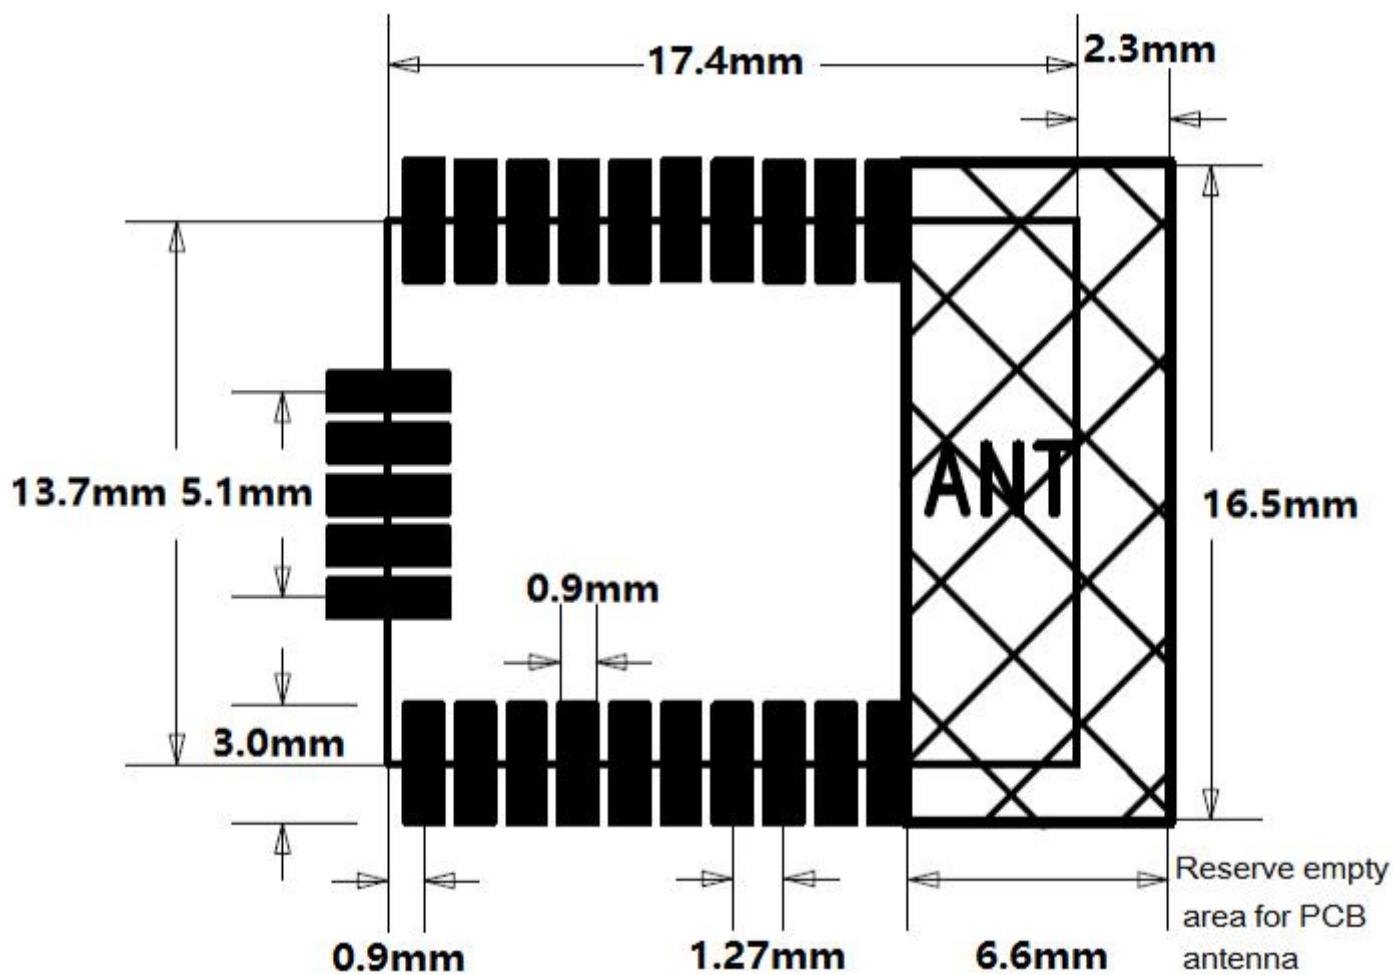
推荐 PCB 封装/ SKB380 Recommended PCB Footprint
